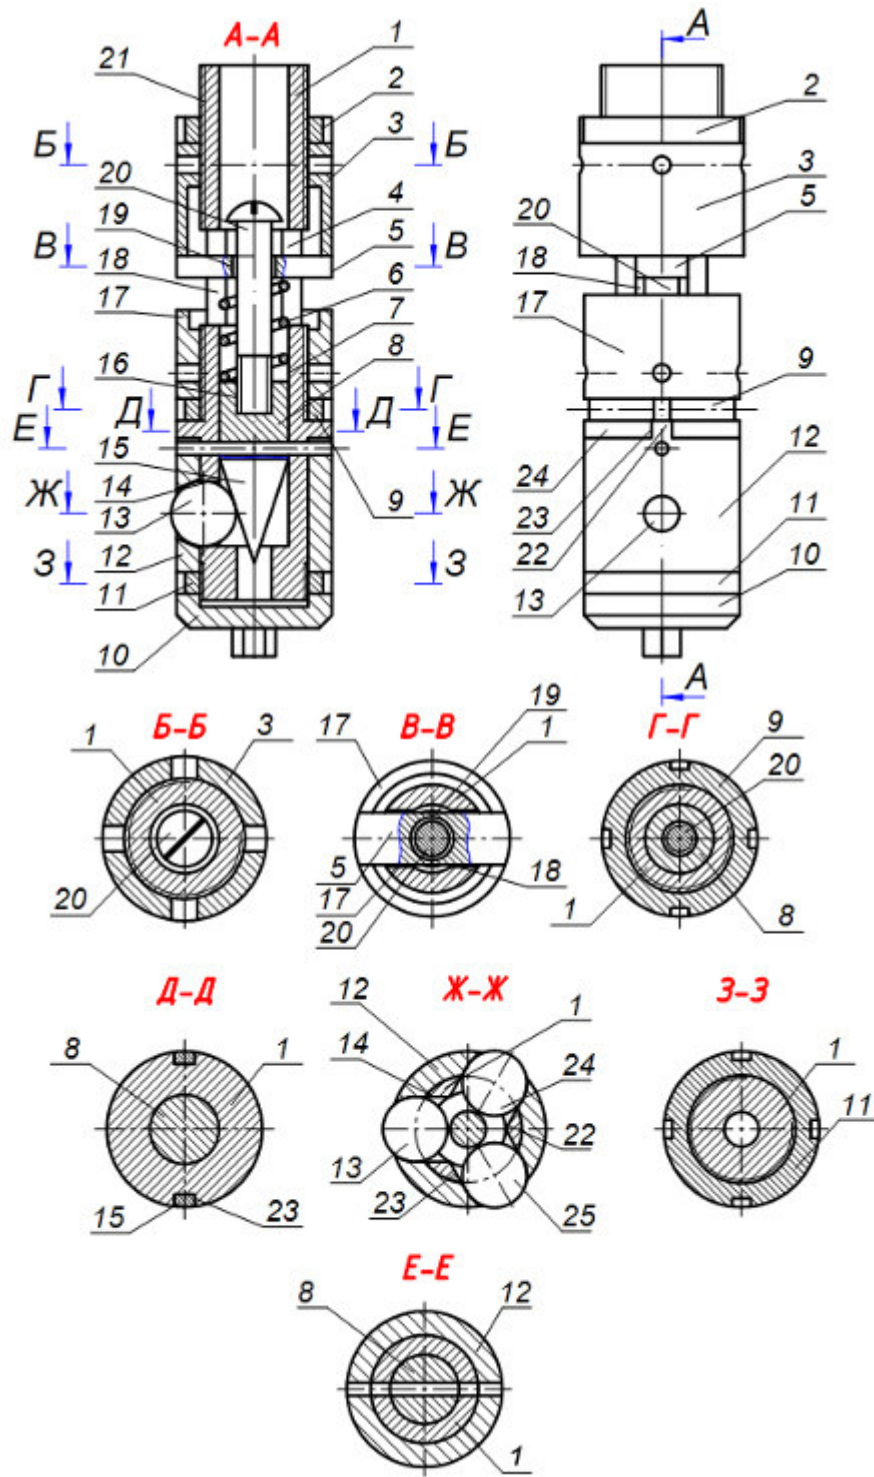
Інструмент для формування регулярного мікрорельєфу віброобробчуванням
